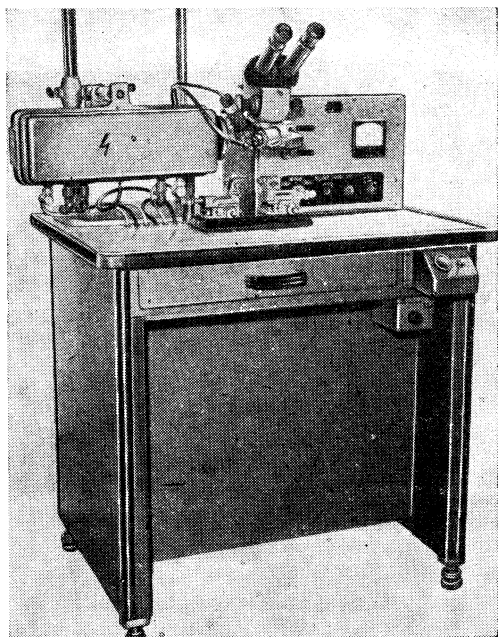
Внешний вид сварочного аппарата С-1.
